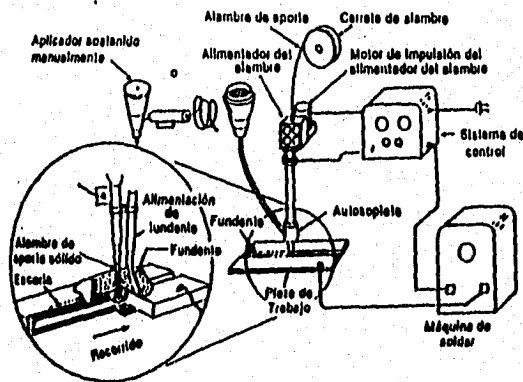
Partes de un sistema para soldadura por arco sumergido
